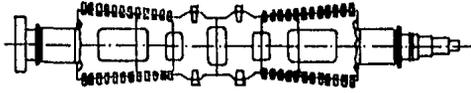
Rotor de TV forjado separadamente en piezas y luego soldadas entre si.
